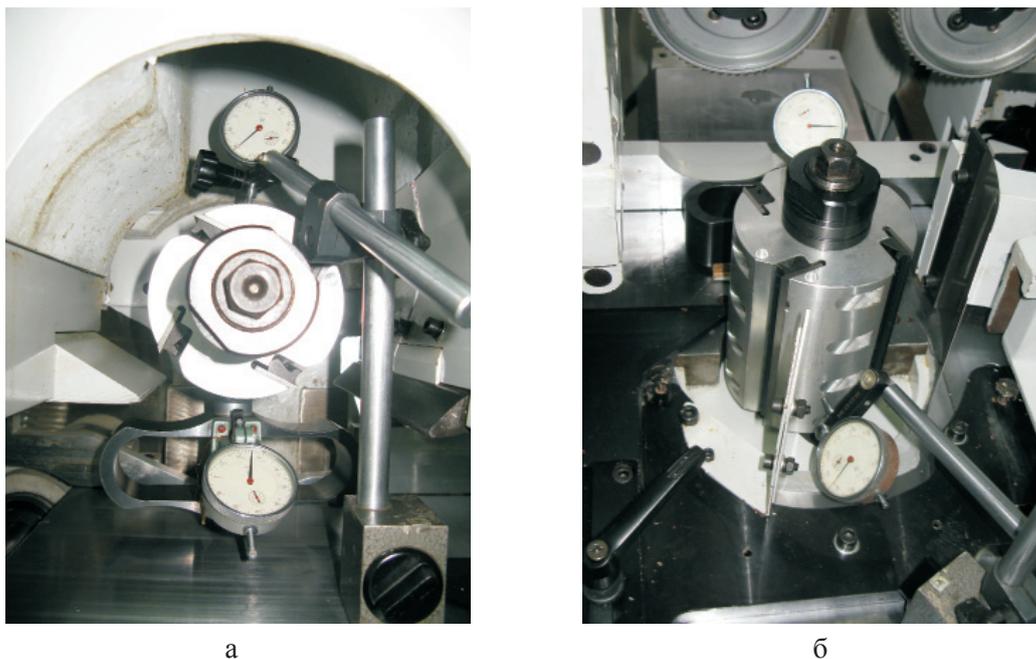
Установка приборов для измерения сил и деформаций на верхней (а) и левой боковой (б) ножевых головках четырехстороннего продольно-фрезерного станка «Beaver 523»
